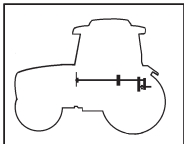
Si nécessaire, pousser en avant le palier de l'arbre arrière et dégager le manchon de raccordement des 2 arbres arrière de la P.d.F.
